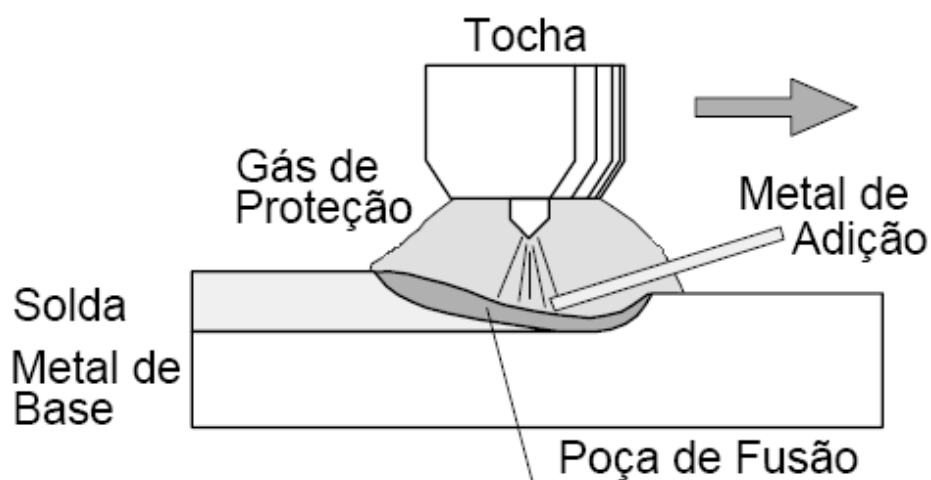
Desenho esquemático do processo de soldagem TIG (MODENESI, 2006)
